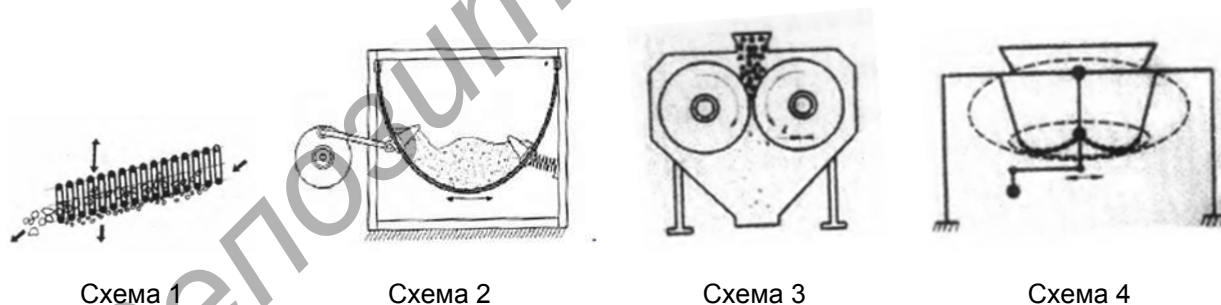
Адаптивные механизмы с кинематикой движения рабочих органов
